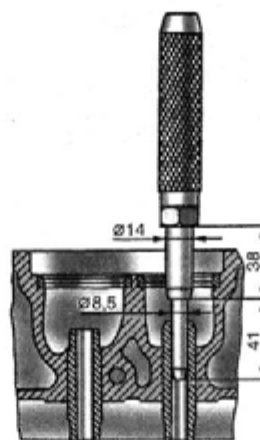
Выпрессовка направляющих втулок клапанов
